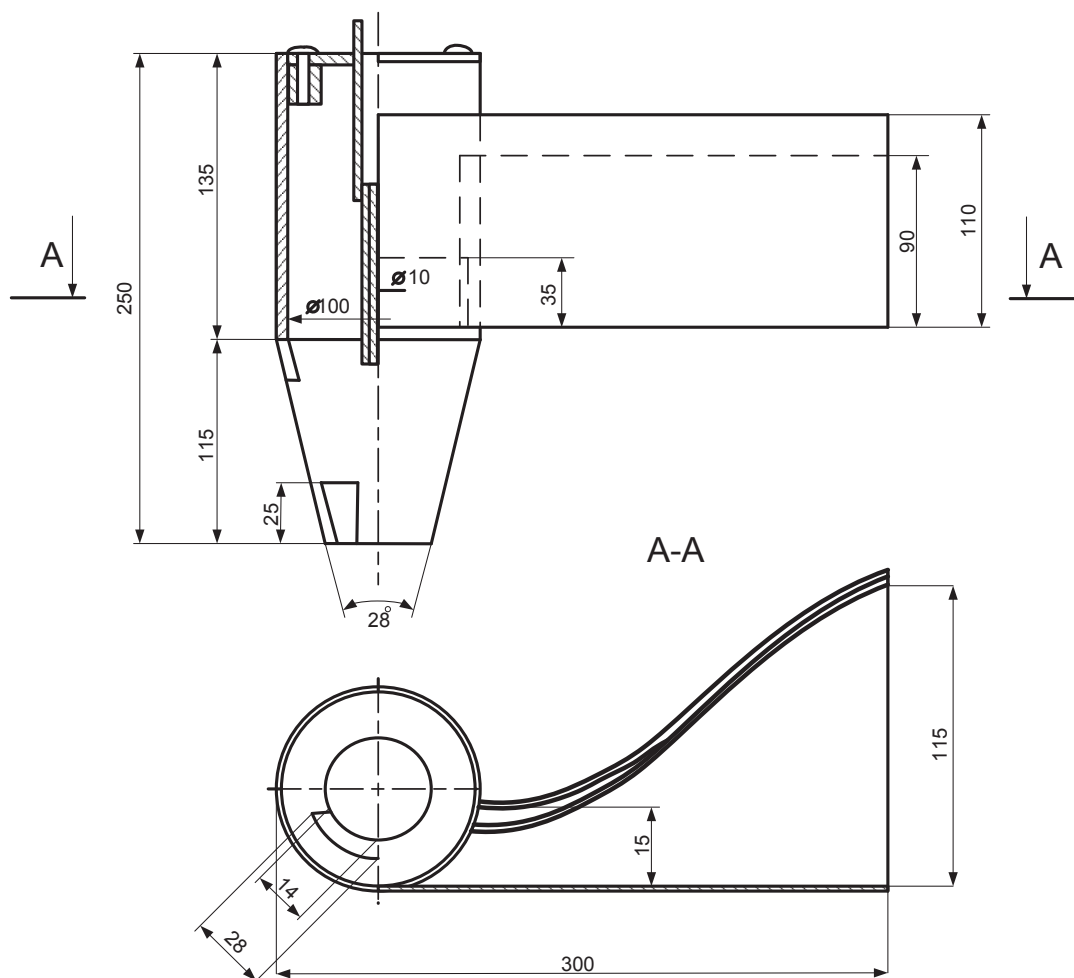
Чертеж конструктивно-подобной модели БГЦ
